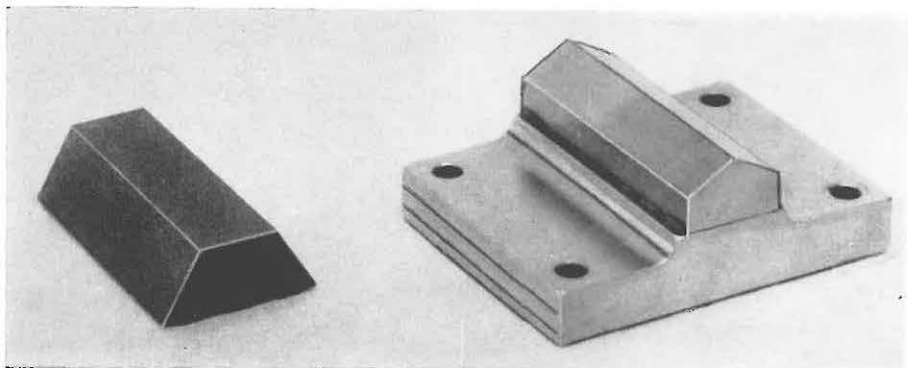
Schneide mit Grundkörper (rechts) und Lagerfläche (links)
